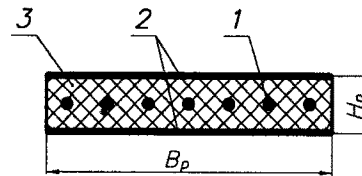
Конструкция кордшнуровых плоских ремней: 1 - кордшнуры; 2 - обкладки; 3 - резиновый наполнитель
